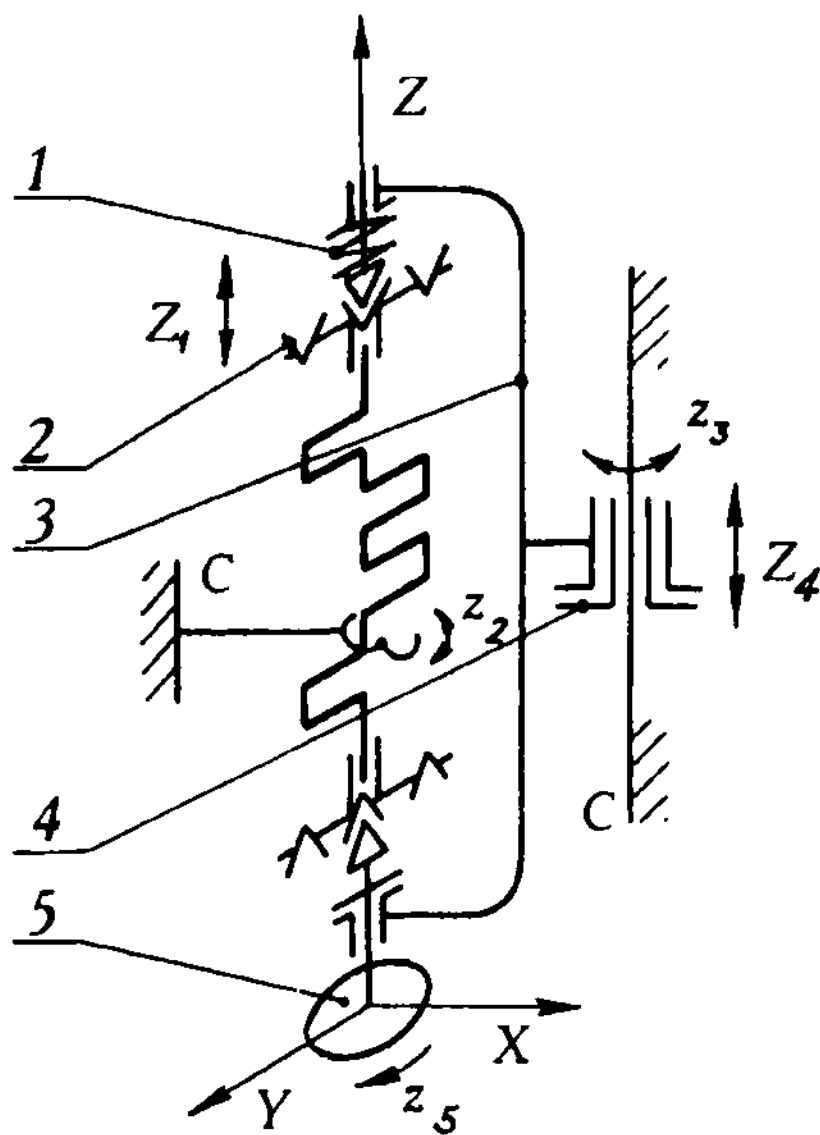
Схема станка для закалки шеек коленчатого вала:
